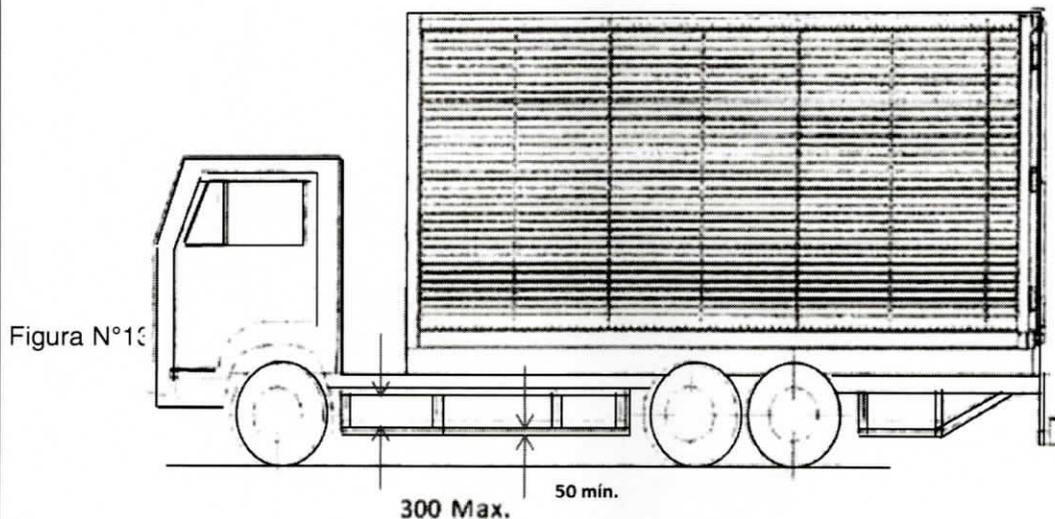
, Dimensiones de los largueros, Vista Lateral (dimensiones en mm)
